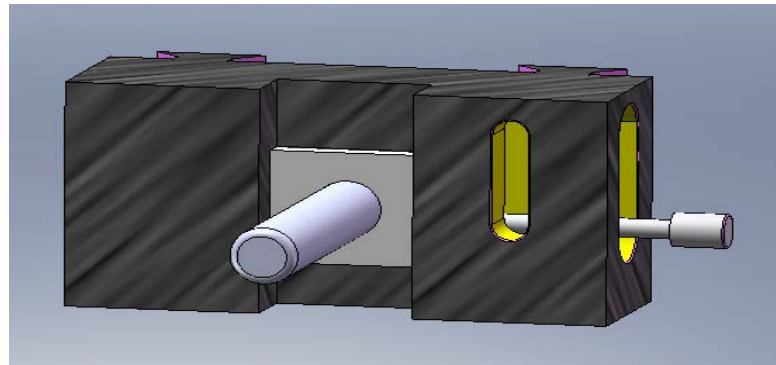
Зміна інструмента IP500 ПМФ4
